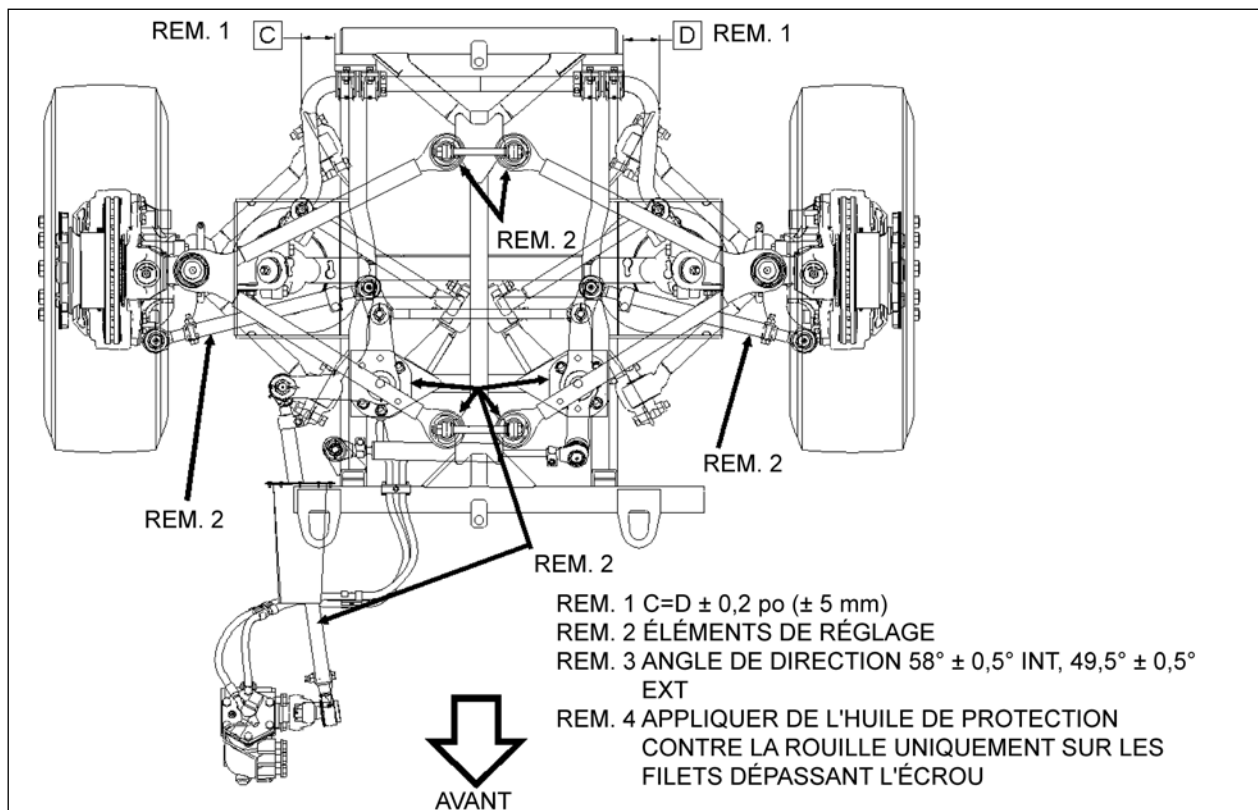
LA REMARQUE 2 INDIQUE OÙ LE RÉGLAGE DOIT ÊTRE EXÉCUTÉ AU BESOIN EN PROCÉDANT À LA GÉOMÉTRIE IFS.
